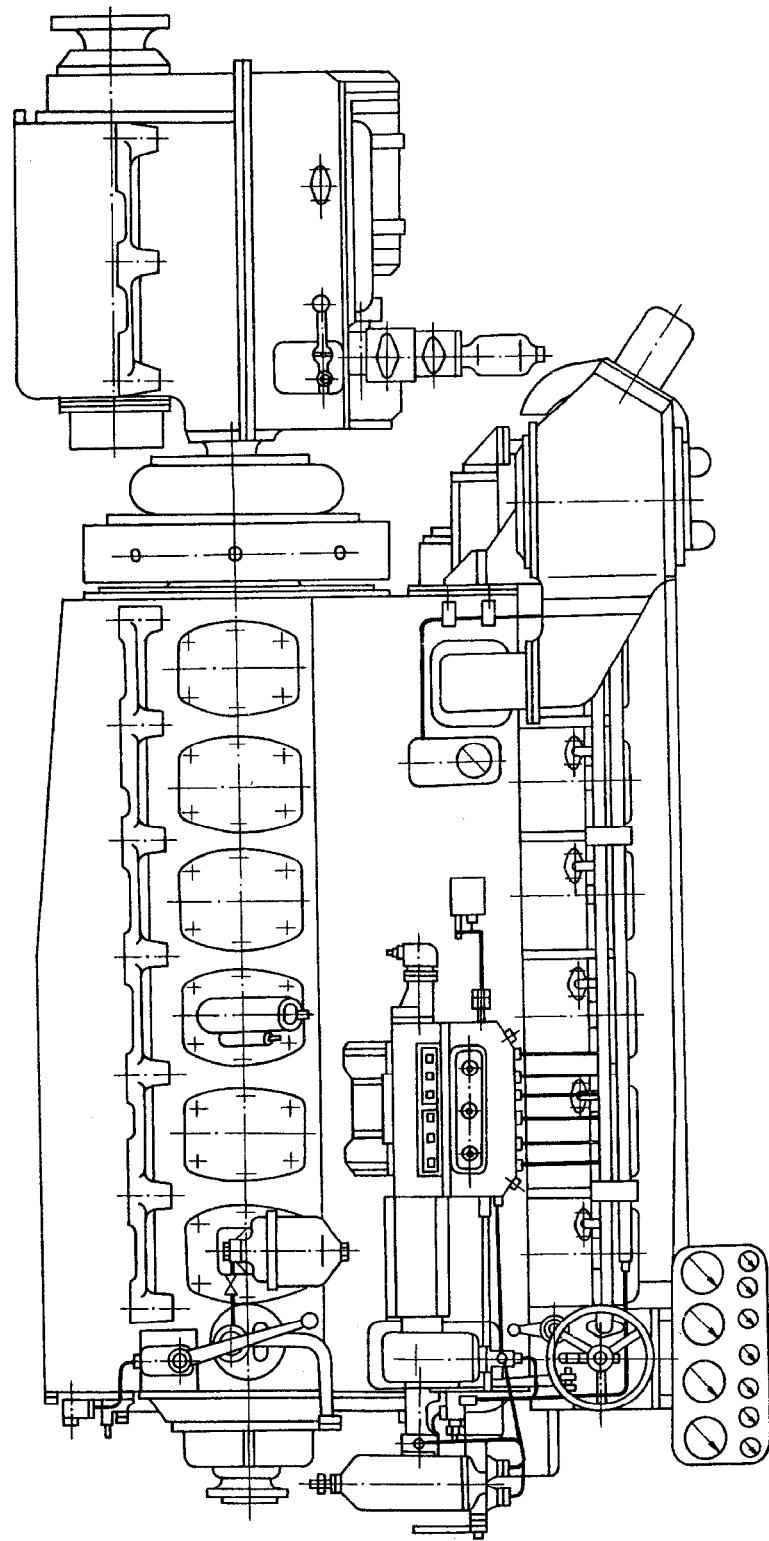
Дизель-редукторный агрегат 6ЧПН2А 18/22-225-1 /общий вид/
